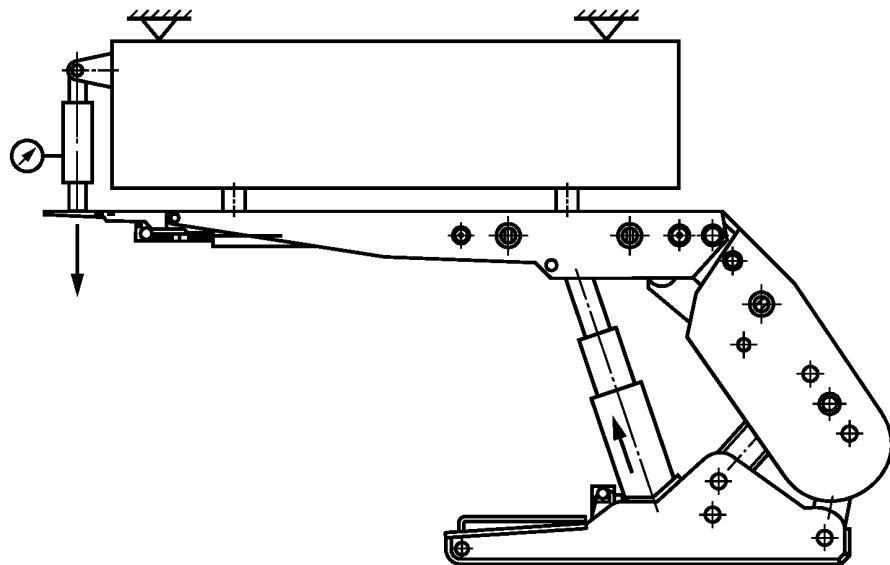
Схема нагружения для определения сопротивления на конце составной гидроподжимной консоли перекрытия
